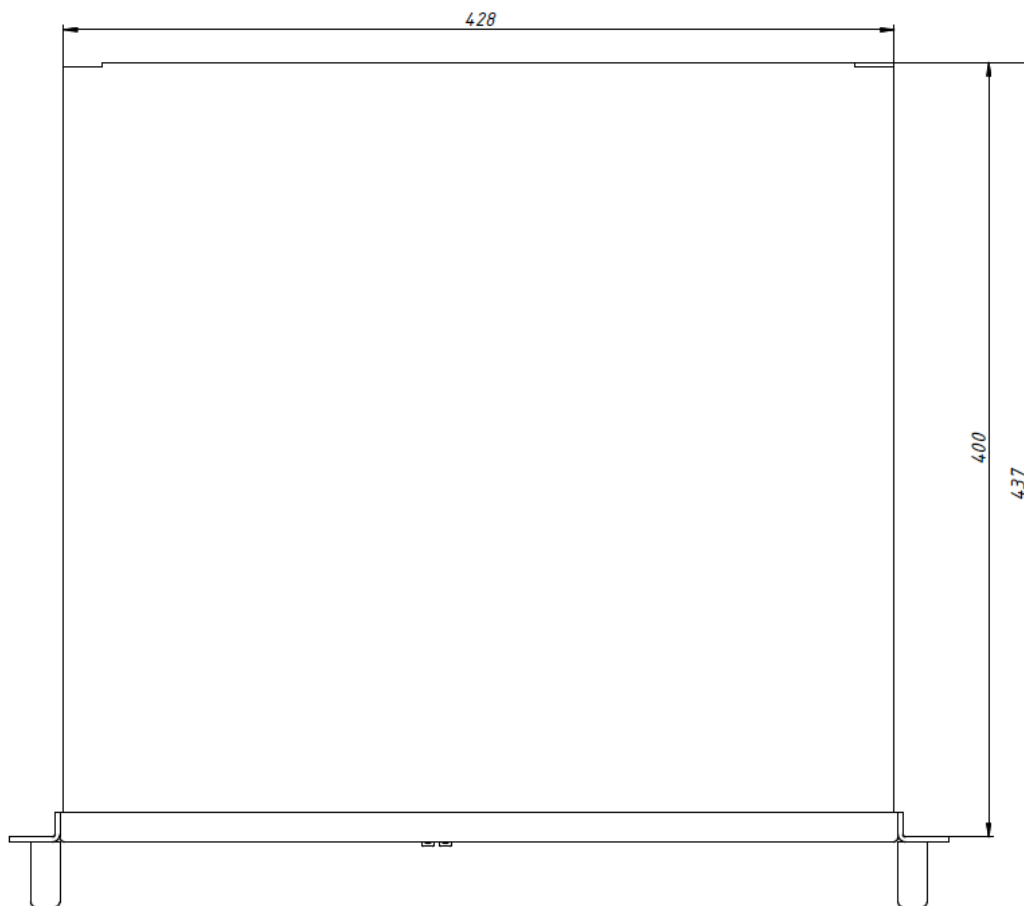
габаритный чертёж ПРК, вид сверху
